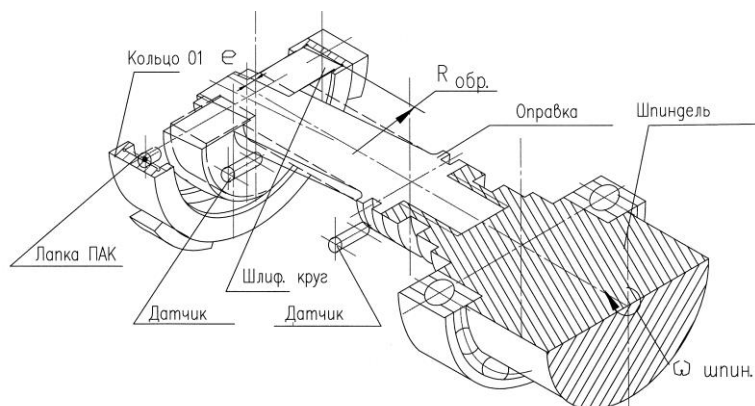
Схема бесцентровой внутренней обработки дорожки качения наружного кольца 01 цилиндрического роликоподшипника
